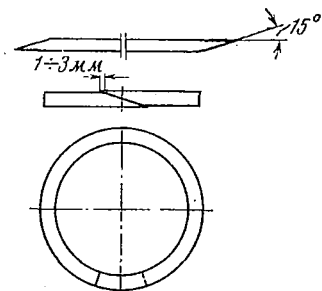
Разрезной уплотнитель из полоски фторопласта-4.
